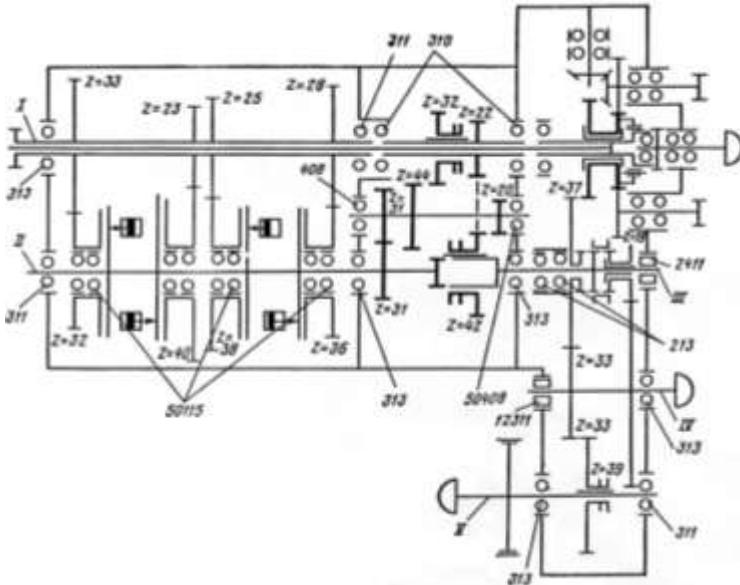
Кинематическая схема коробки передач и раздаточной коробки трактора Т-150К
